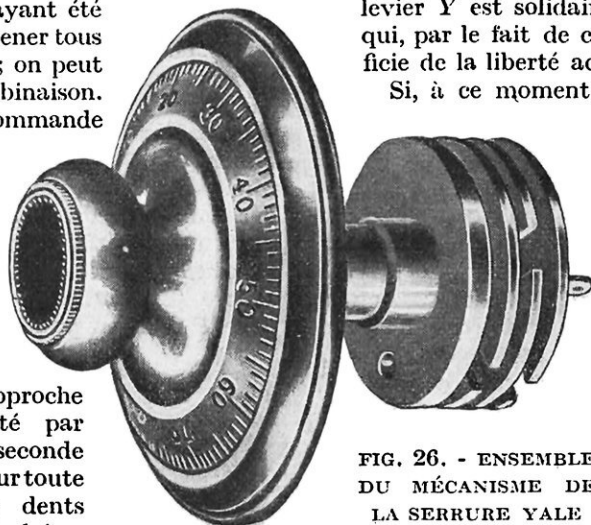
ENSEMBLE DU MÉCANISME DE LA SERRURE YALE
